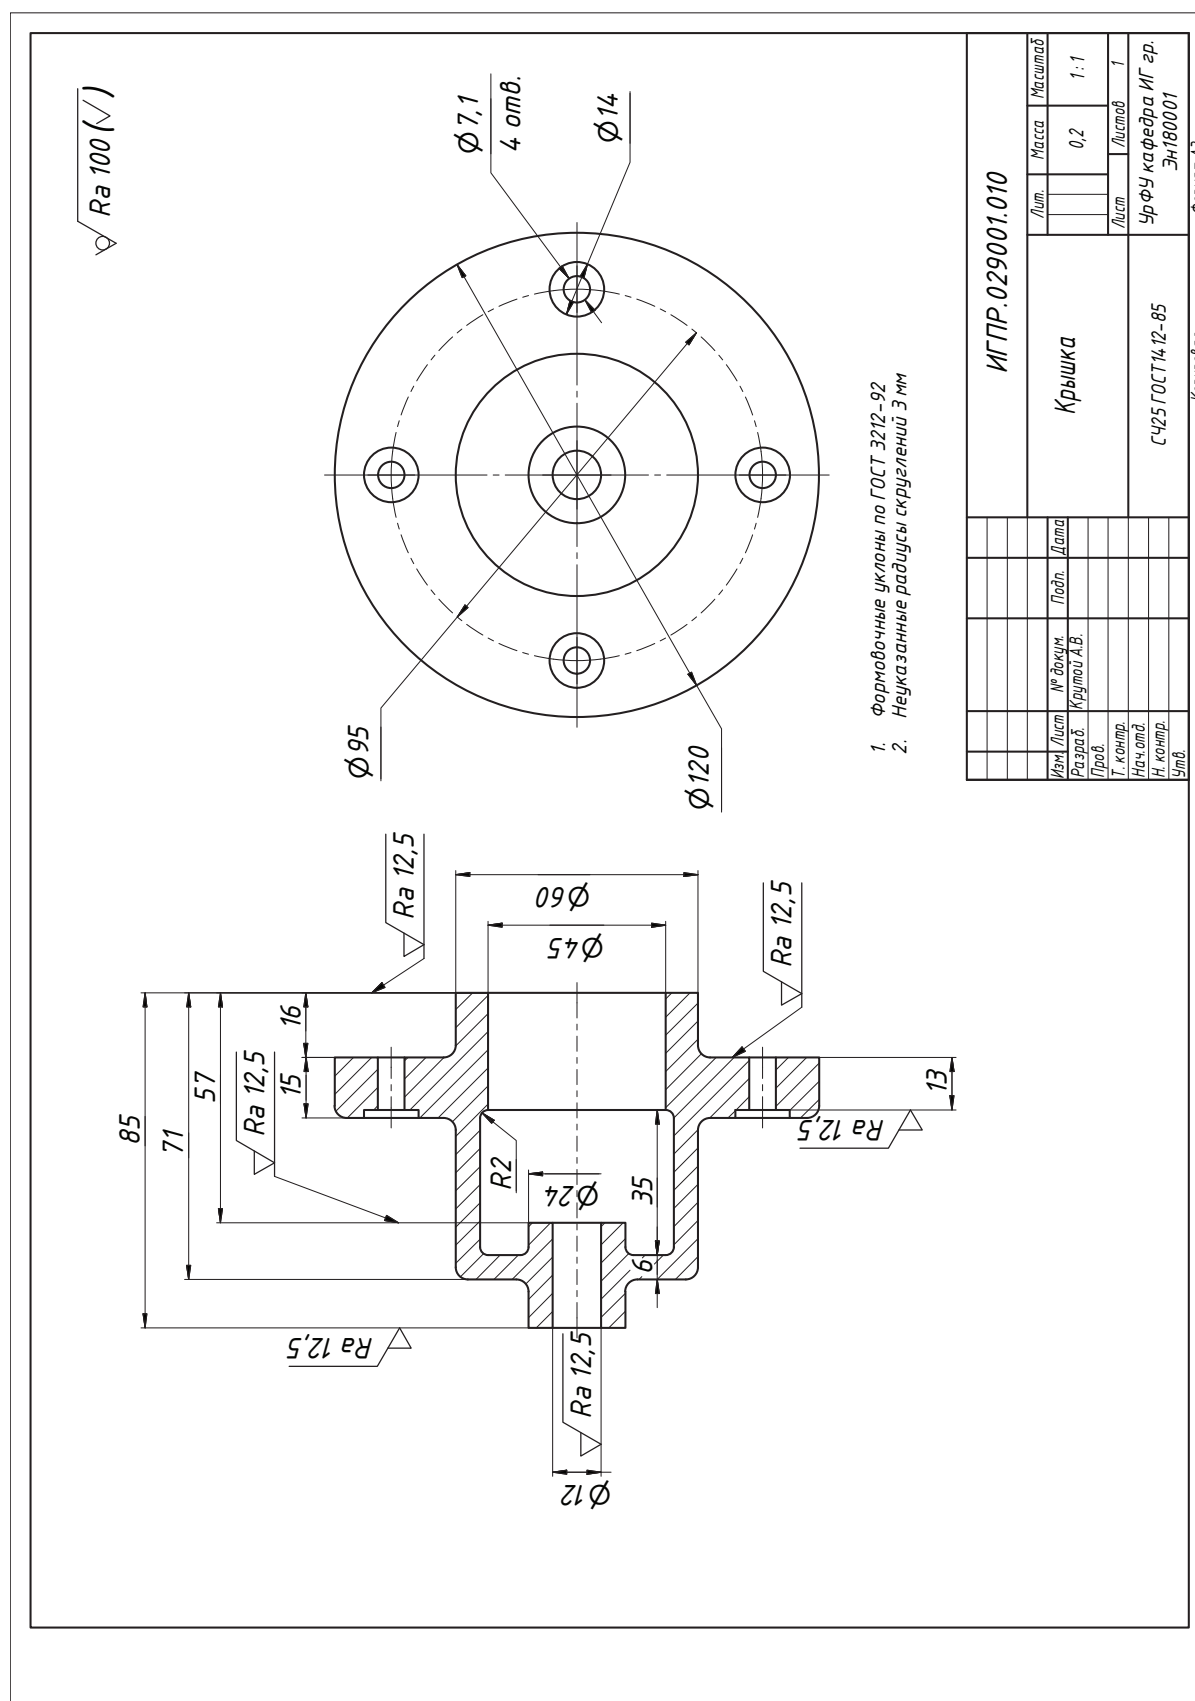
Рабочий чертеж литой детали «Крышка»
